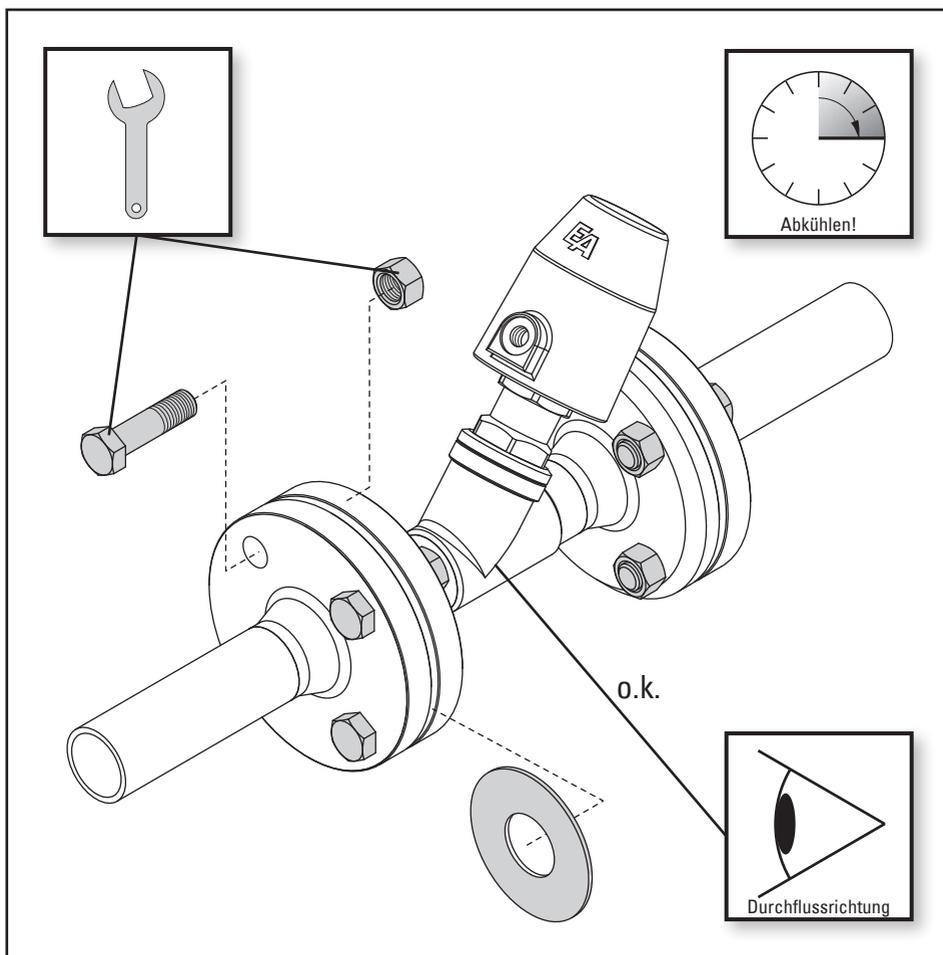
Montage / Demontage - Flanschanschluss
